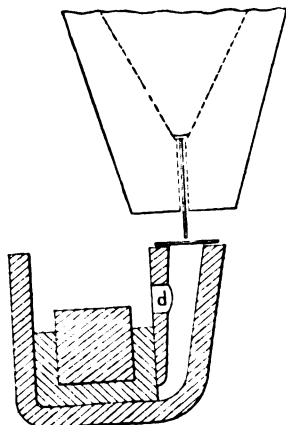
Soudure de deux barres carrées avec éclisse.
